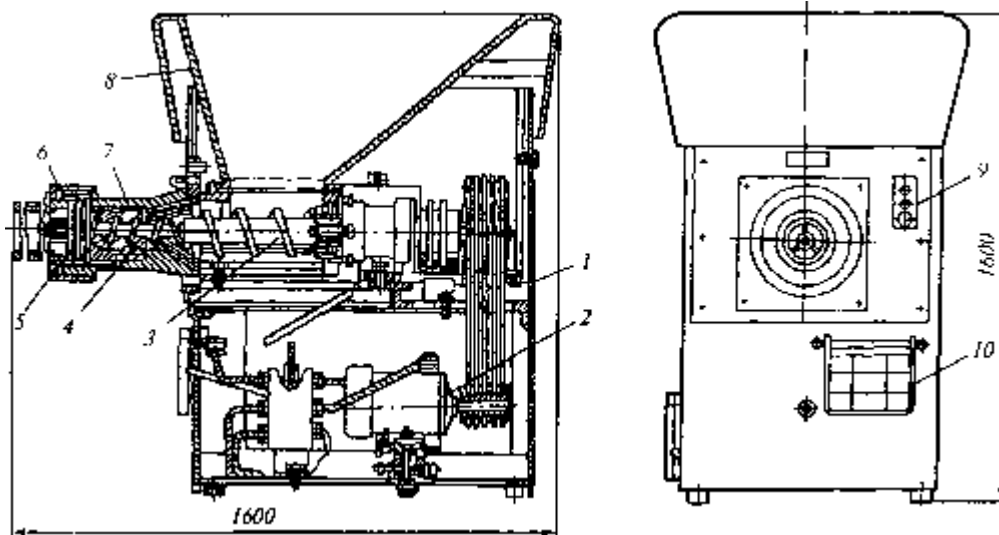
Вовчок К6-ФВП-120: 1 – станина; 2 – привод; 3 – робочий шнек; 4 – допоміжний шнек; 5 - ріжучий механізм; 6 – притискний пристрій; 7 – циліндр; 8 – бункер; 9 – кнопки управління; 10 – відкидна планка.
